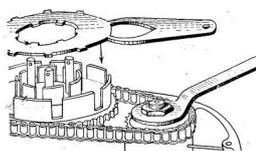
Фиксация звездочки коленчатого вала и барабанов сцепления.
